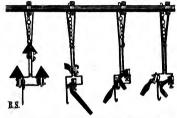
Detail zur Universal-Hackmaschine von Rud, Sack, Leipzig-Plagwits.
